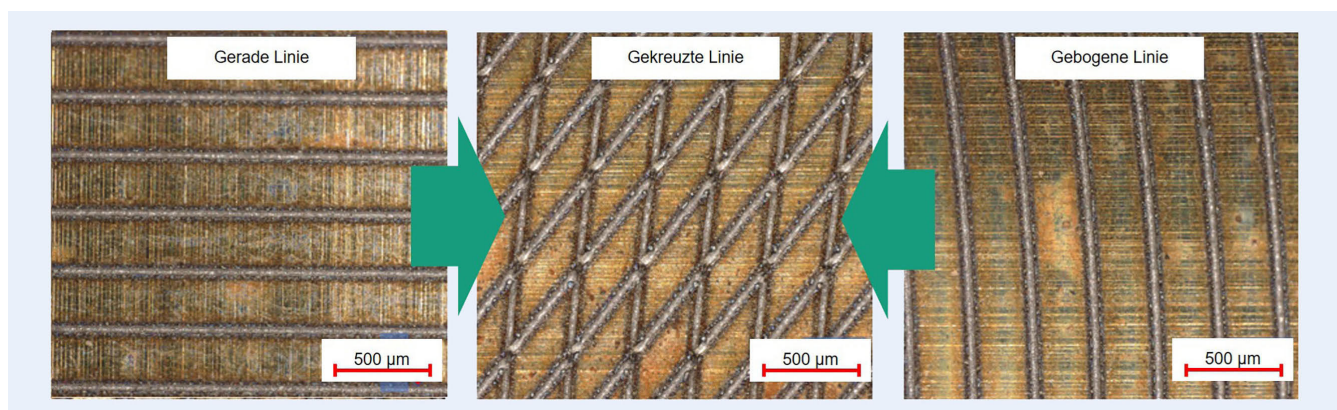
Erarbeitete Laserstrukturen auf den Rührreißschweißwerkzeugen. Grafik: Fraunhofer IPA
